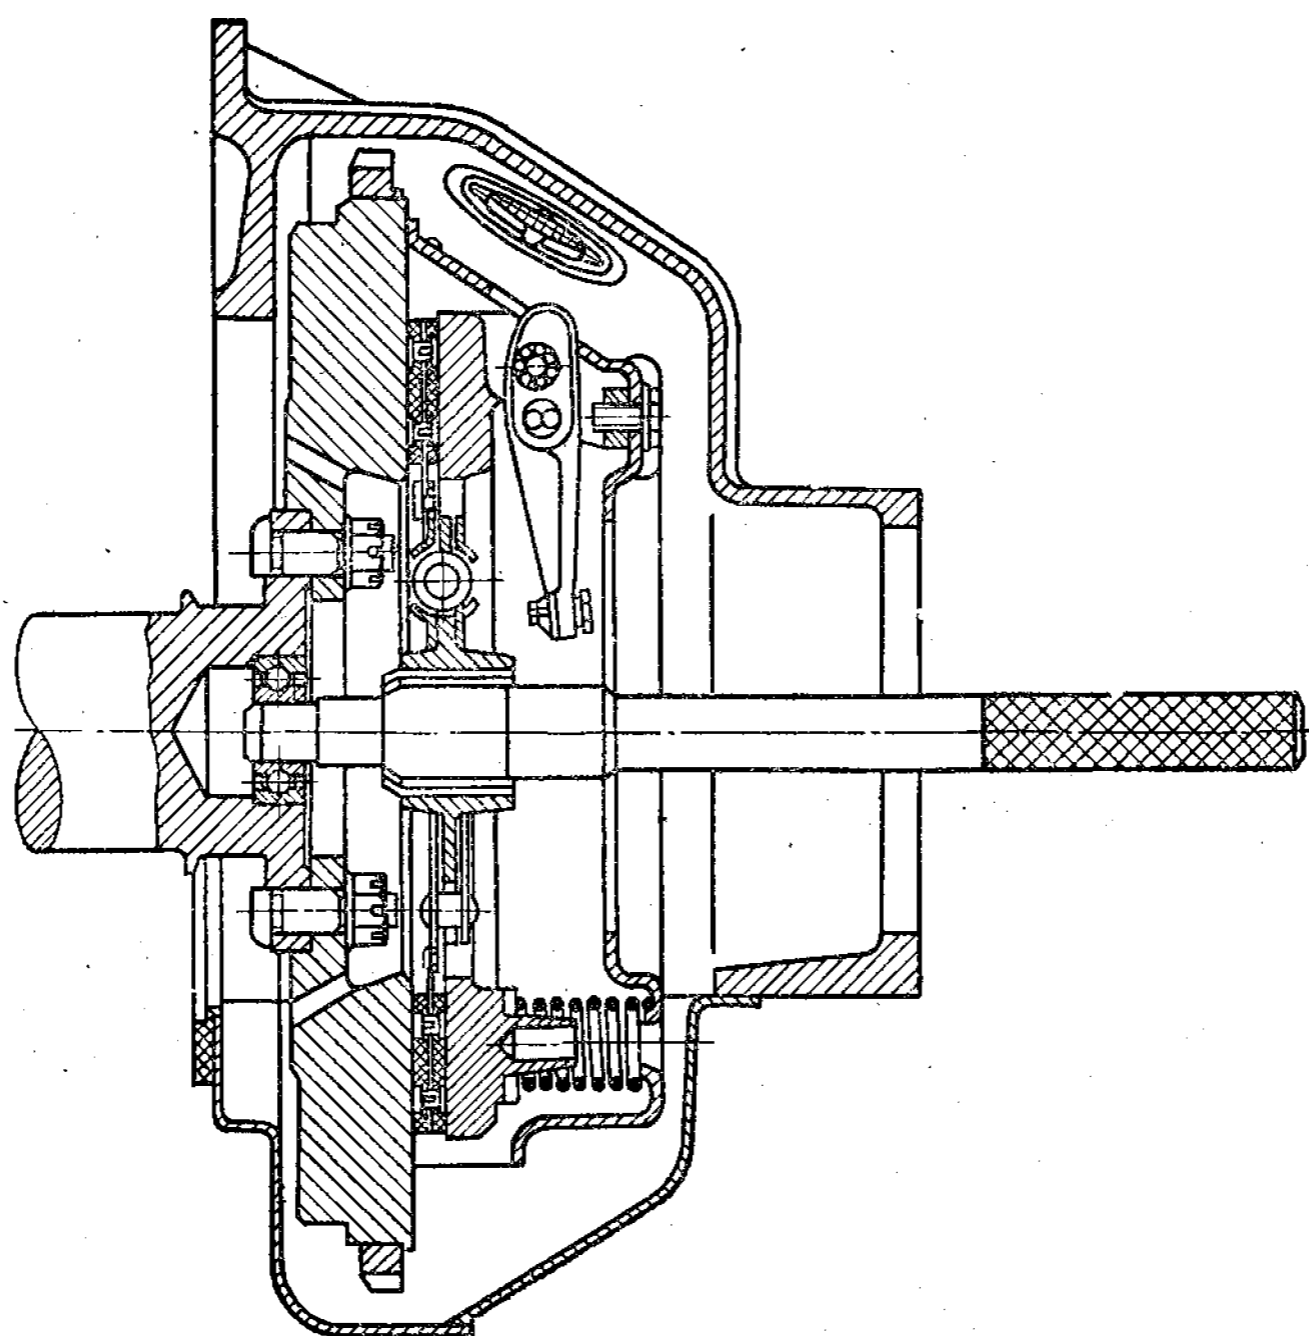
Центровка ведомого диска сцепления при установке на двигатель
